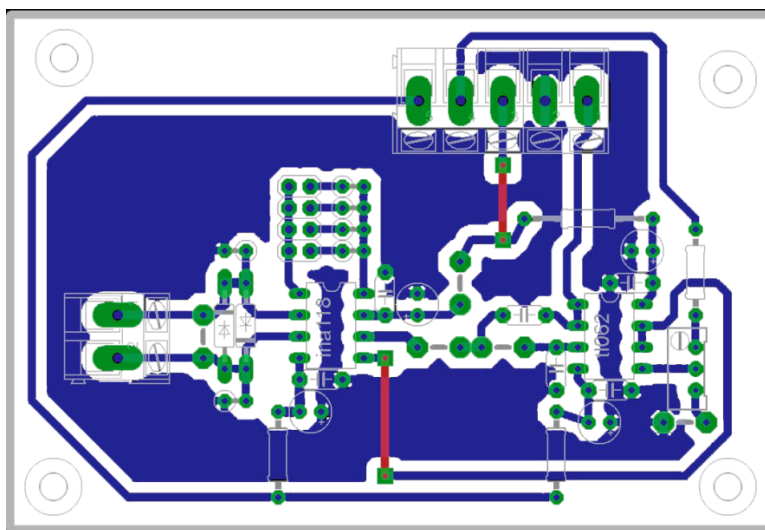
PCB del sistema acondicionador de señal del sensor sísmico
